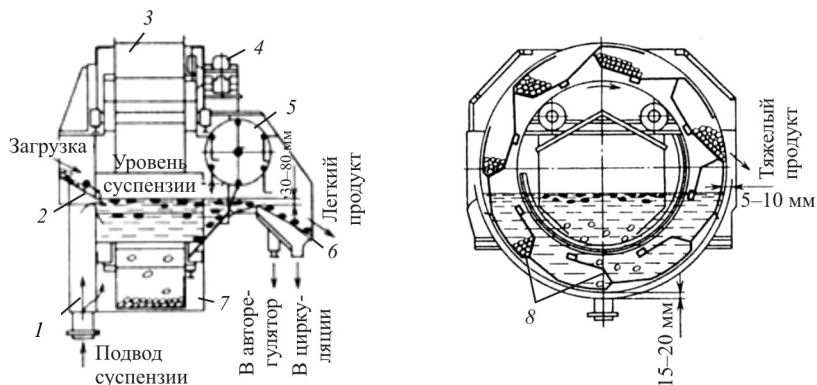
Устройство тяжелосреднего колесного сепаратора: 1 – нижний патрубок; 2 – загрузочный желоб; 3 – вертикальное элеваторное колесо; 4 – привод; 5 – гребковый механизм; 6 – разгрузочная часть ванны для легких фракций; 7 – разгрузочная часть ванны для тяжелых фракций; 8 – ковши элеваторного колеса
